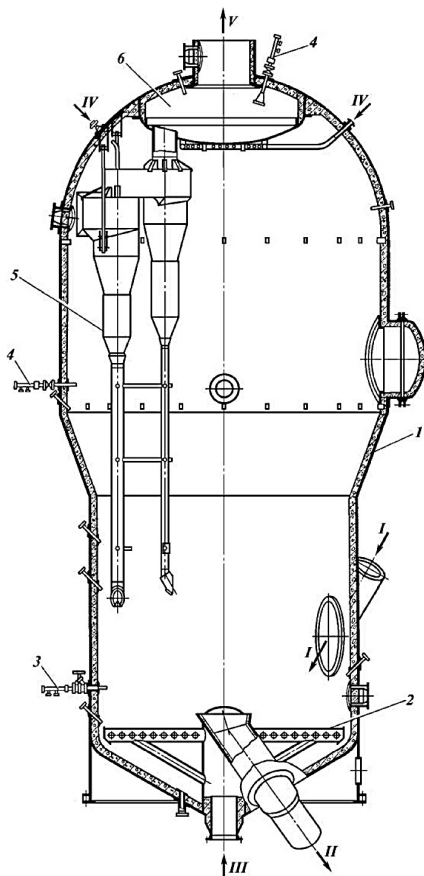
Регенератор с пылевидным катализатором: 1 — корпус; 2 — коллектор для ввода воздуха; 3 — топливная форсунка; 4 — форсунки для конденсата; 5 — двухступенчатые циклоны; 6 — сборная камера. Потоки: I — закоксованный катализатор из реактора; II — регенерированный катализатор; III — воздух; IV — водяной пар; V — дымовые газы
